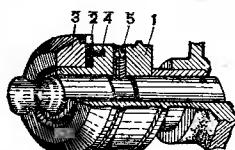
Зубчатый барабан в кинопроекторе П16П1: 1 — корпус; 2 — зубчатый венец; 3 — реборда; 4 — штифт; 5 — винт крепления
